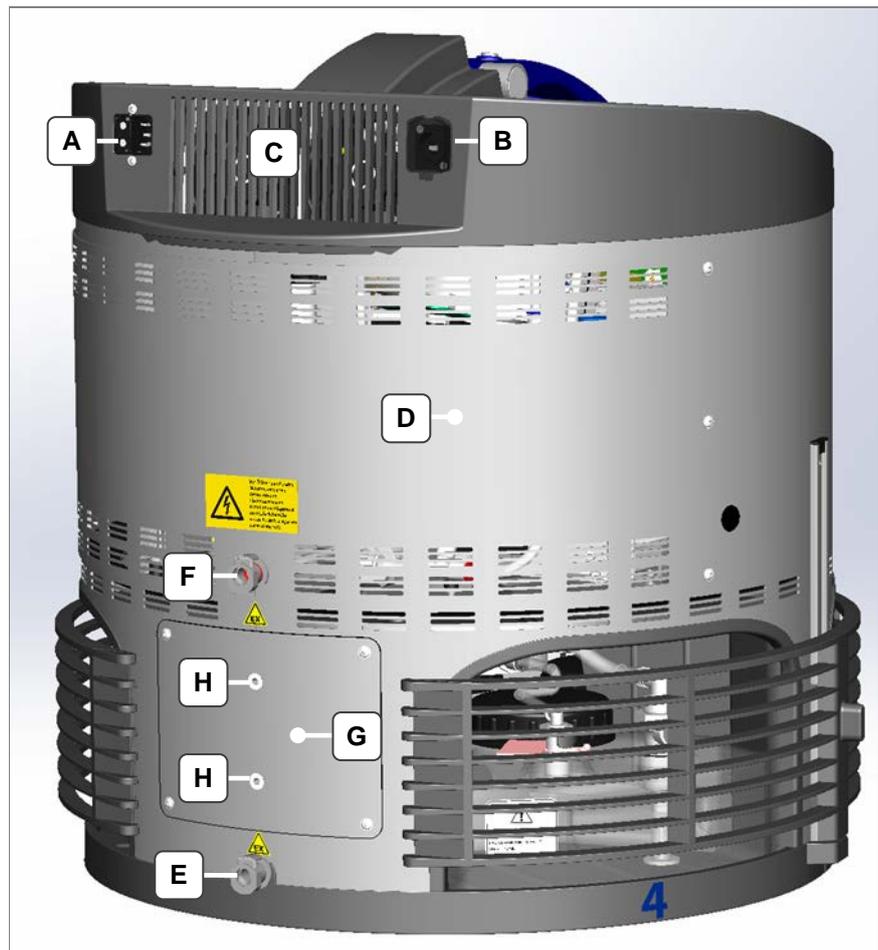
Vue arrière de la machine à nettoyer
